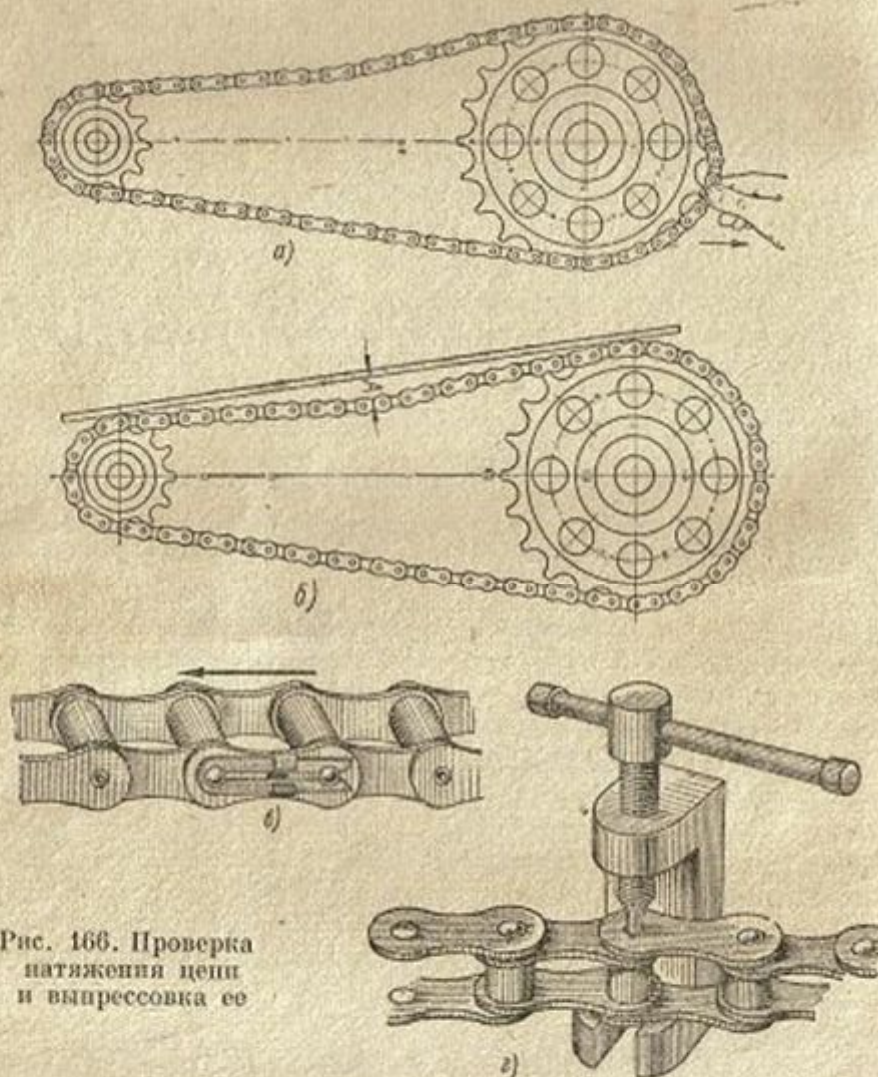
Проверка натяжения цепи и выпрессовка ее
